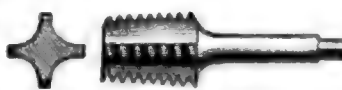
u. 15. Gewindebohrer für hölzerne Schrauben. a Querschnitt.
